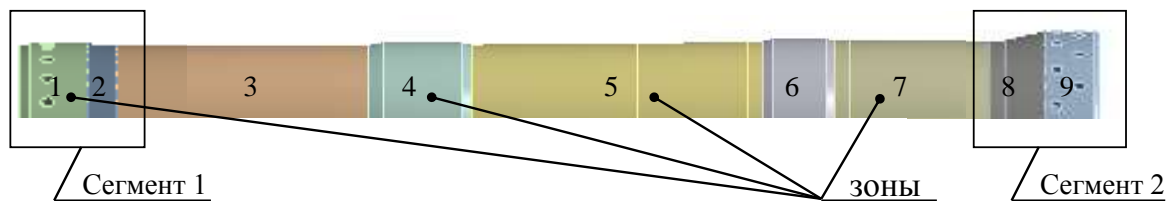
3D-модель крупногабаритной многослойной конструкции
